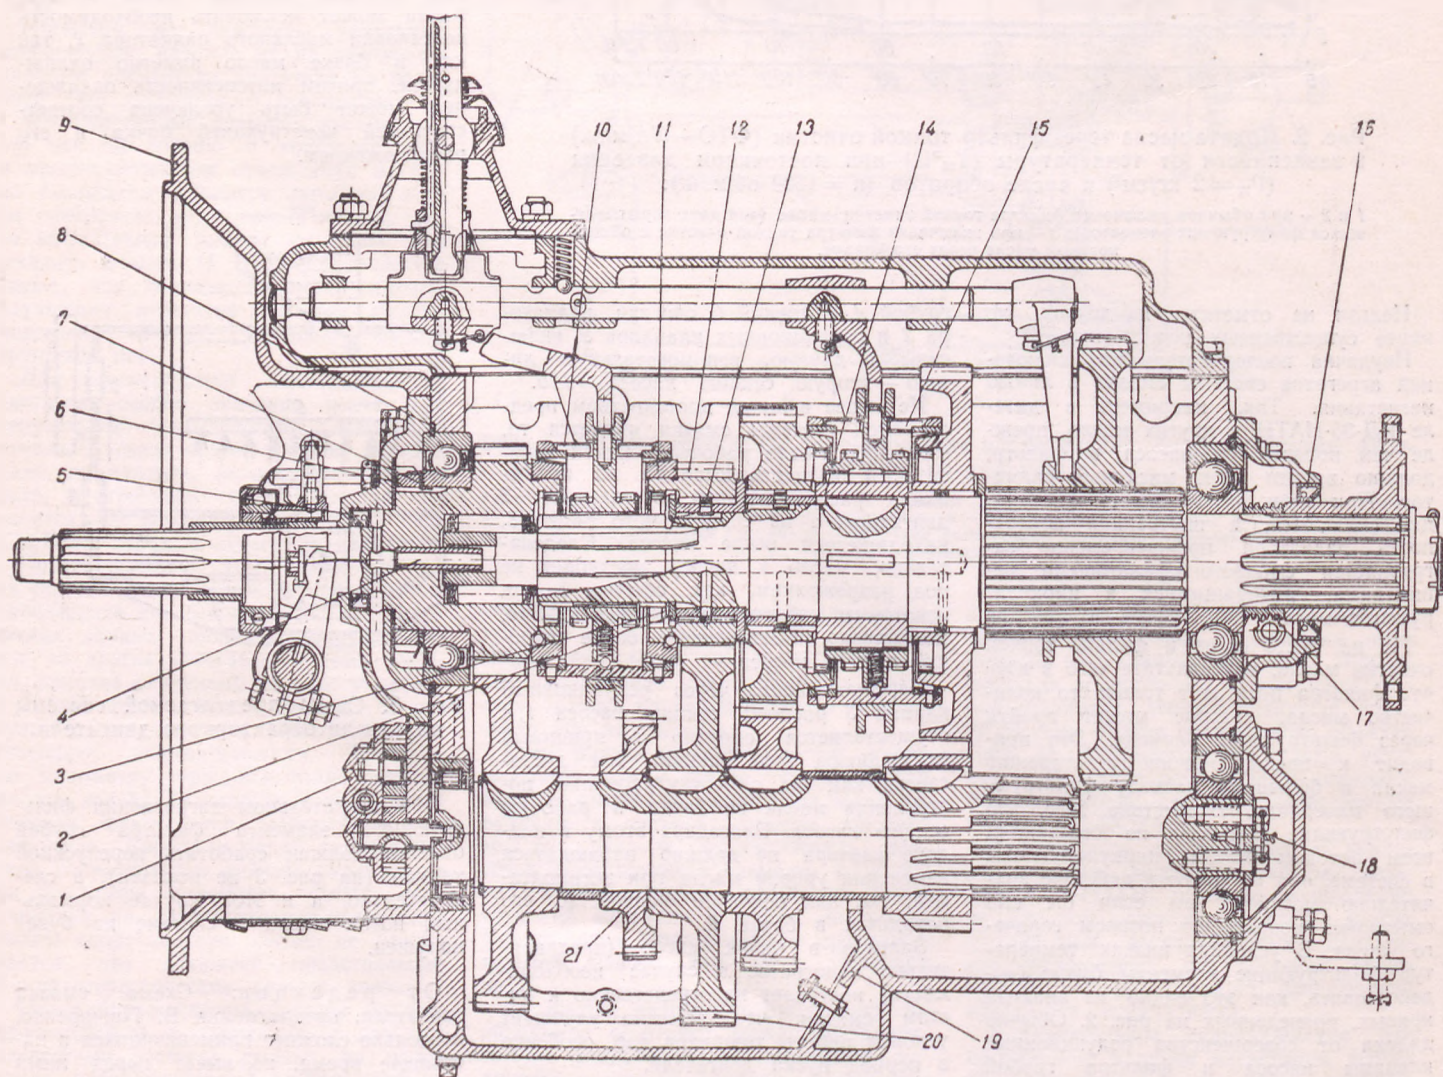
Общий вид коробки перемены передач (продольный разрез):
